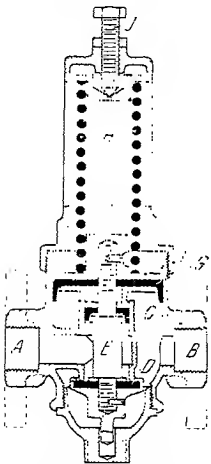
Druckregler von C. W. J. BLANCKE & Co.
